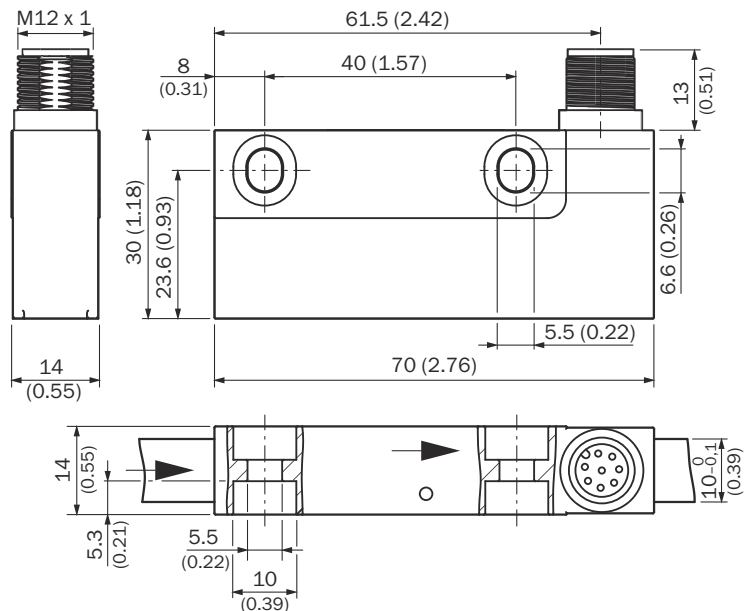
Disegni quotati TTK70S con connettore maschio M12 (tutte le dimensioni in mm)
